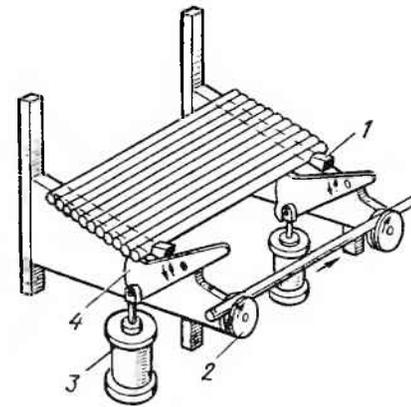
Механизированный стеллаж для подачи прутков к ножницам: 1 — ограничитель, 2 — приводной рольганг, 3 — пневмоцилиндры, 4 — рычажный отсекатель
